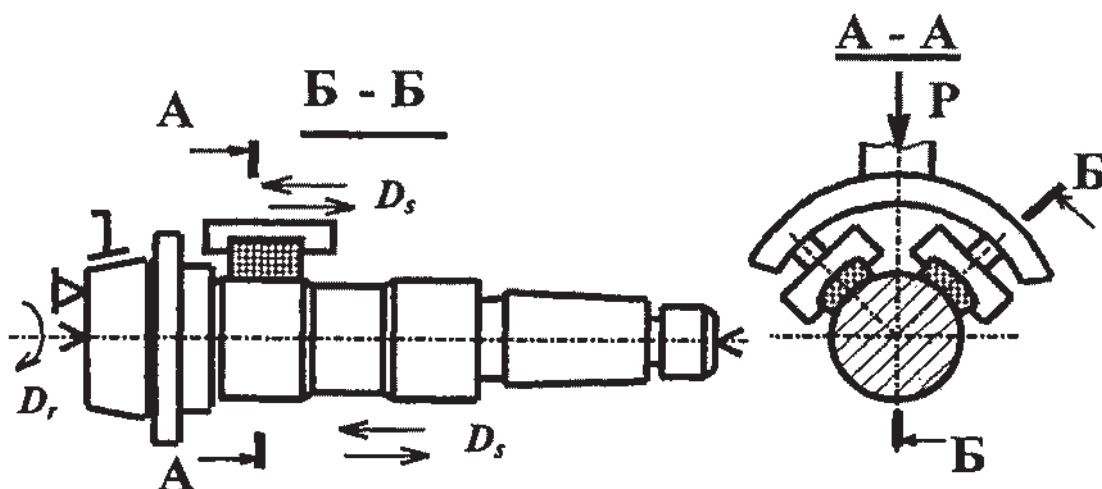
Схема суперфиниширования наружной цилиндрической поверхности
